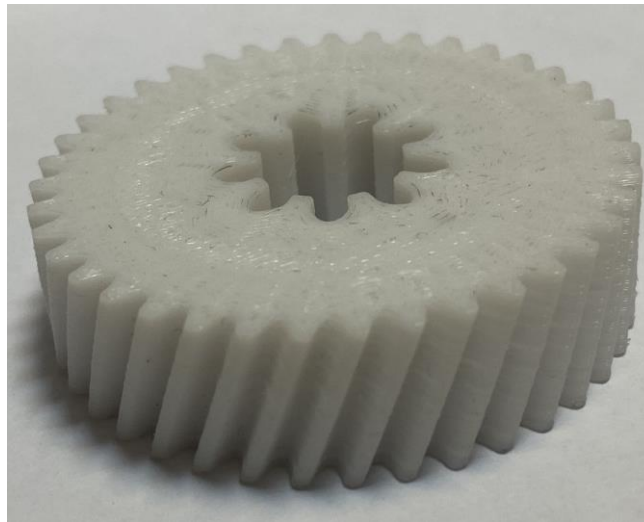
Шестерня редуктора, из материала PETG
